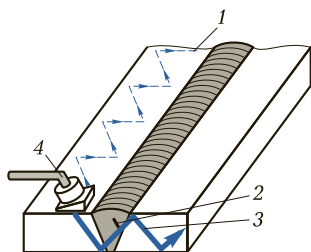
Схема ультразвуковой диагностики сварного шва при наличии в нем трещины:
